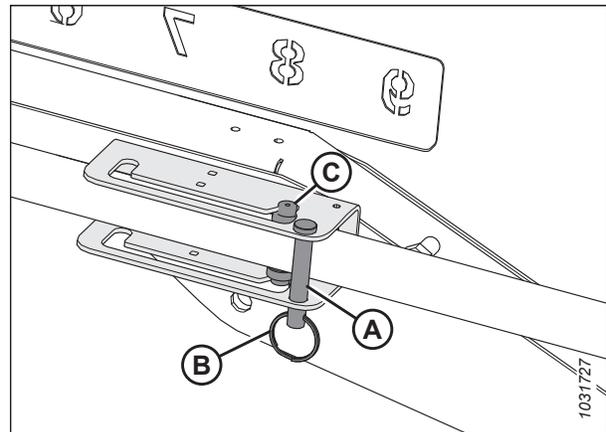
Cilindro del braccio sinistro – Posizione arretrata
